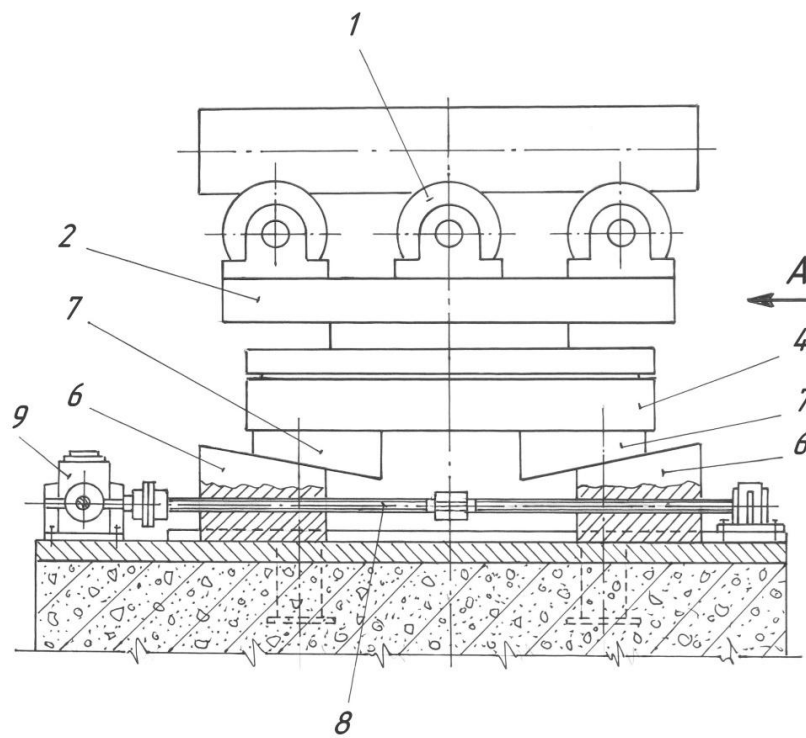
Загальний вид модернізованої конструкції поворотного рольгангу
